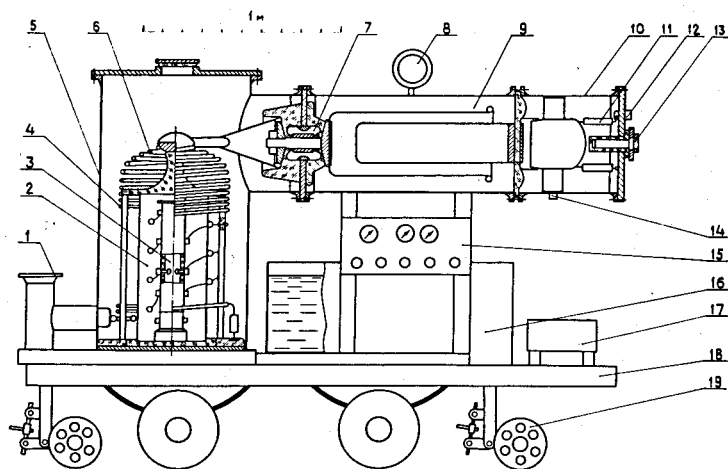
Эскиз конструкции генератора с ГИН-500-0,02/5.
